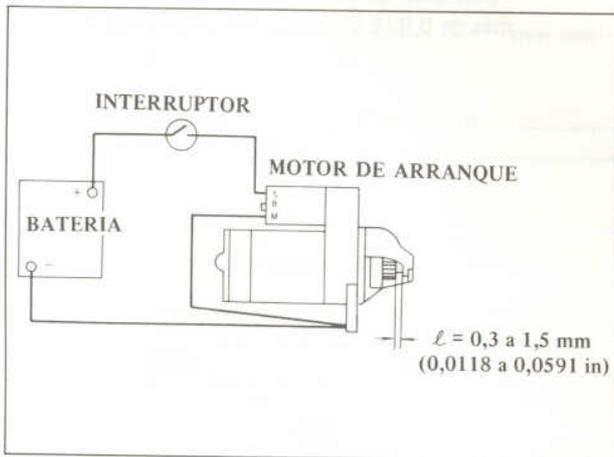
Circuito de prueba del conjunto del interruptor magnético
